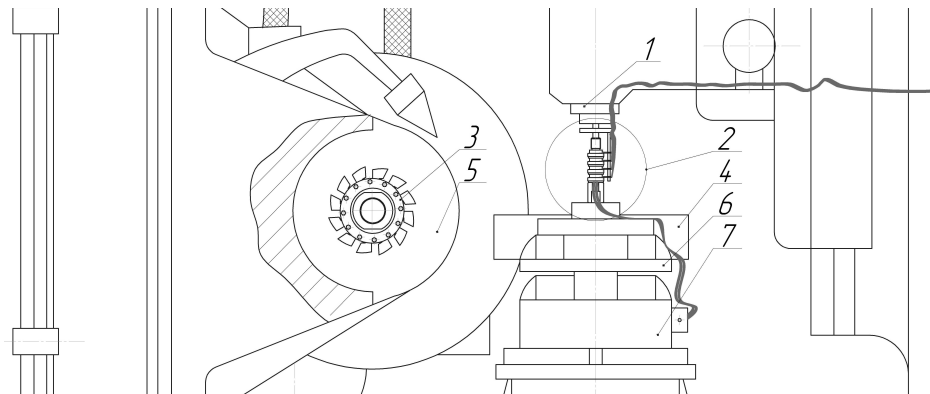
Эскиз приспособления для закрепления образцов, имитирующих одну впадину зубчатого колеса
